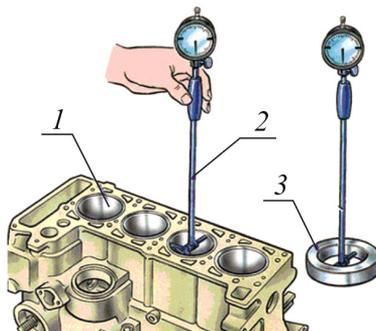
Ручное измерение цилиндров: *1* – блок цилиндров; *2* – нутромер; *3* – калибр
